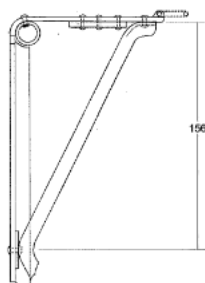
Vista da parte inferior do suporte metálico (medida em mm)
